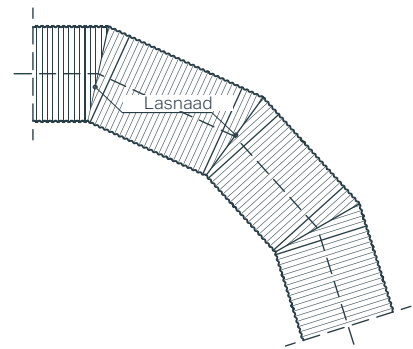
Segmentbocht in een constructie - bovenaanzicht
